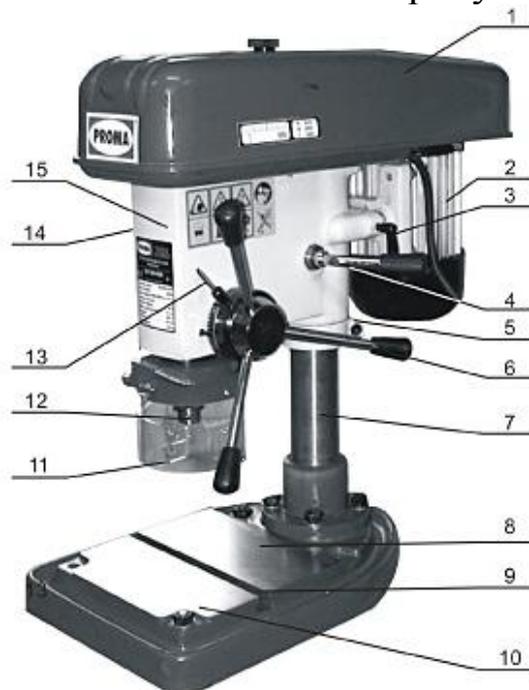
Настольно-сверлильный станок: 1 – крышка; 2 – электродвигатель; 3 - зажимной болт двигателя; 4 - зажимной болт для установки высоты коробки шпинделя; 5 - опорное кольцо; 6 - ручка подачи шпинделя; 7 – опора; 8 - чугунное основание; 9 - Т – образный паз; 10 - болт для крепления к столу; 11- защитный экран; 12 – шпиндель; 13 - стопорный болт для установки глубины сверления; 14 - панель управления; 15 - коробка шпинделя
